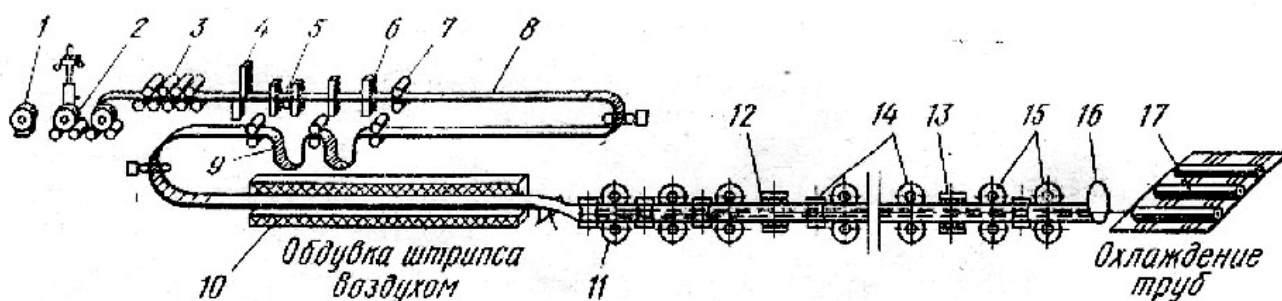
Схема непрерывного агрегата 1/2—2" для печной сварки труб
